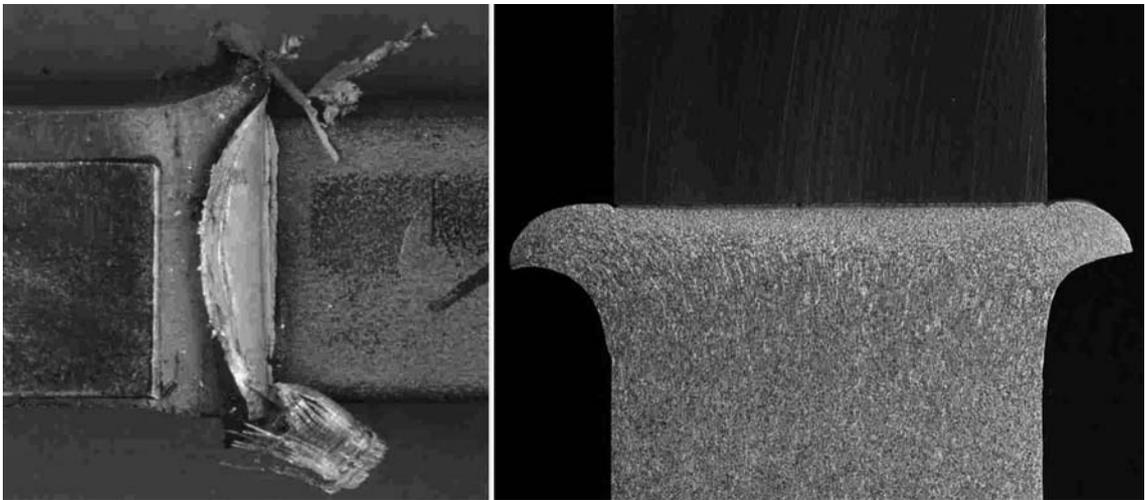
Querschliff einer Orbitalreißschweißverbindung der Werkstoffkombination AlMg4 mit X6CrNiMoTi17-12-2 am Querschnitt 20x20 mm
